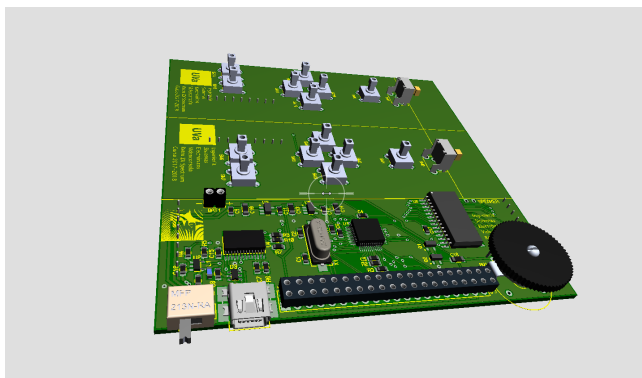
Vista 3D del diseño de la PCB en la versión 1.0.
